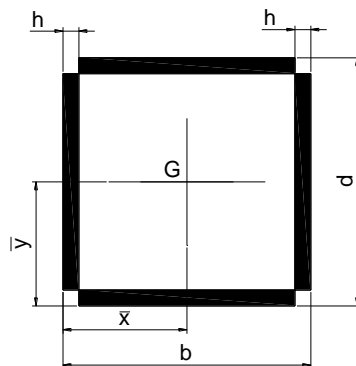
Cordón soldadura anclaje inferior - Chasis
